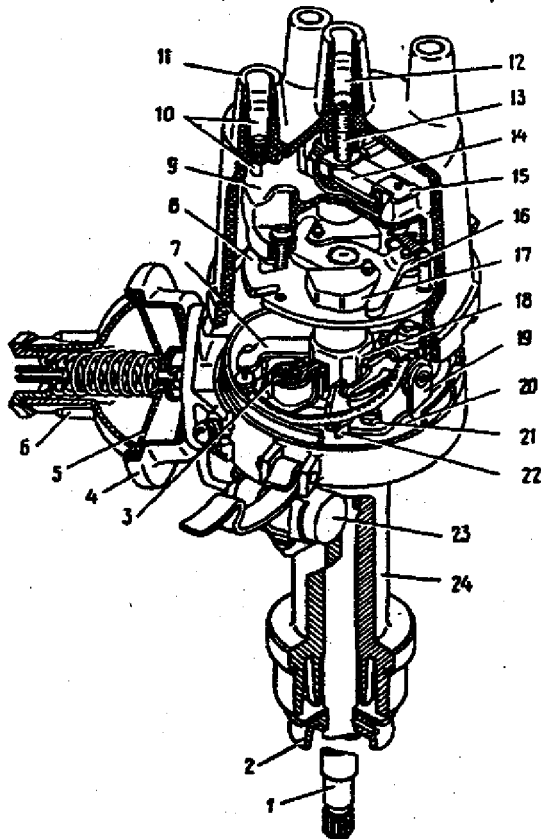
Distribuidor de ignição: 1 - eixo; 2 - defletor de óleo; 3 - feltro de lubrificação; 4 - corpo do regulador de vácuo; 5 - membrana; 6 - tampa do regulador de vácuo; 7 - haste do regulador de vácuo; 8 - placa de apoio do regulador centrífugo; 9 - rotor do distribuidor; 10 - contato da tampa; 11 - tampa; 12 - contato central; 13 - carvão do eletrodo central; 14 - resistor; 15 - contato externo do rotor; 16 - placa do regulador centrífugo; 17 - contrapeso; 18 - came do ruptor; 19 - conjunto do ruptor; 20 - contato móvel do ruptor; 21 - parafuso de fixação e ajuste do ruptor; 22 - ranhura para ajuste; 23 - condensador; 24 - carcaça do distribuidor.
